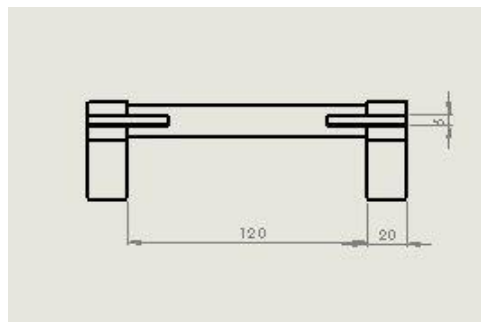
Desain 3 Dimensi Rancangan *Pokayoke Hole Lower A
